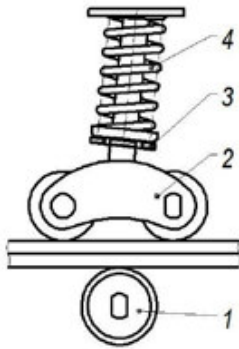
Схема регулировки зажимного транспортера: 1 – поддерживающий ролик; 2 – нажимная каретка; 3 – гайка регулировочная; 4 – пружина
